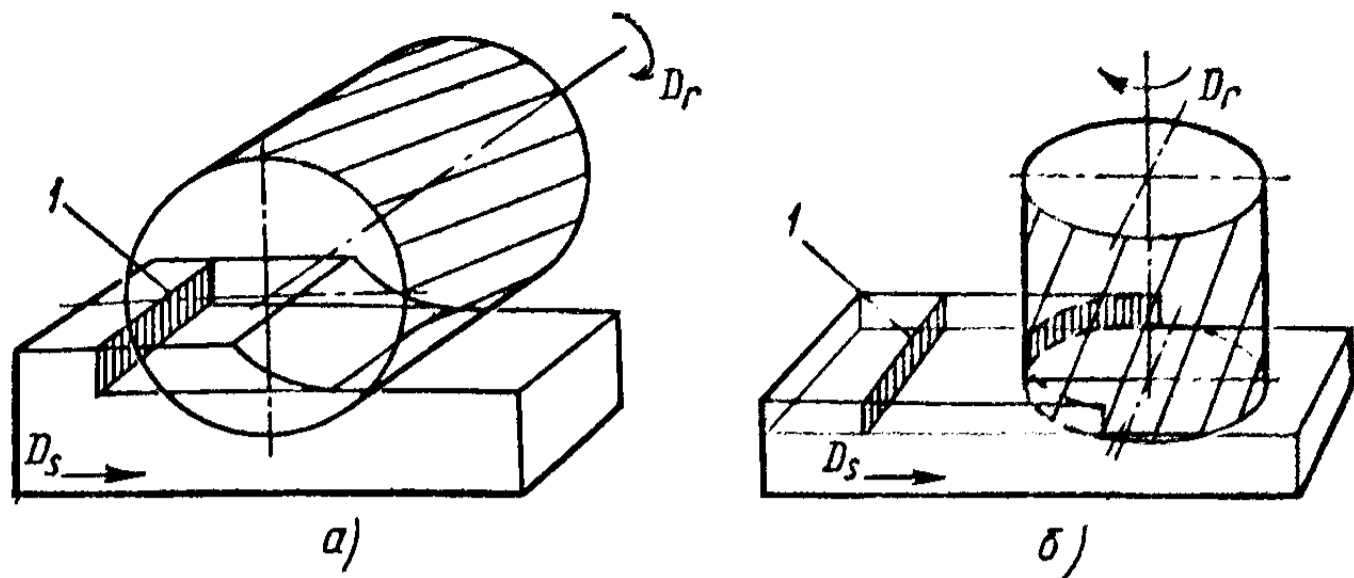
Расположение осей вращения инструментов при фрезеровании на станках:
